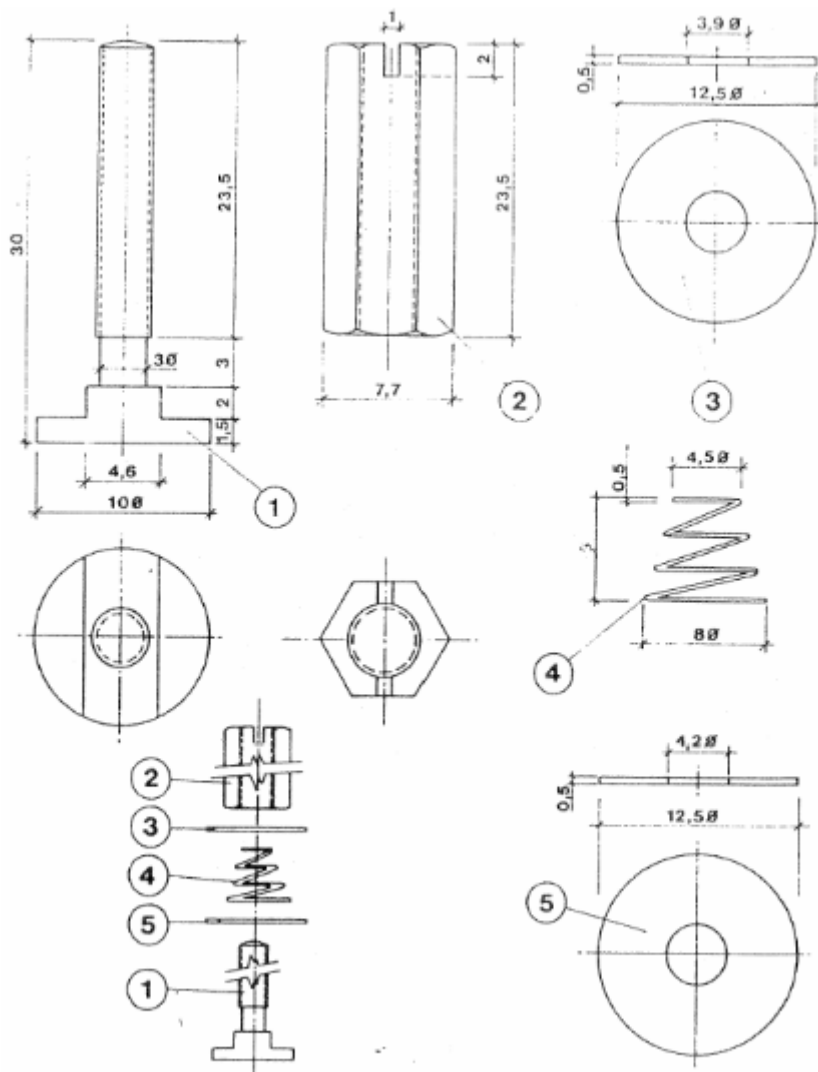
Panel de montaje de contadores. Dimensiones en mm
